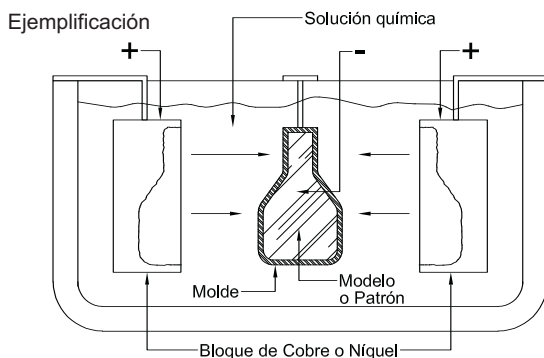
Molde electroformado (Norstar aluminum molds, Inc.)
